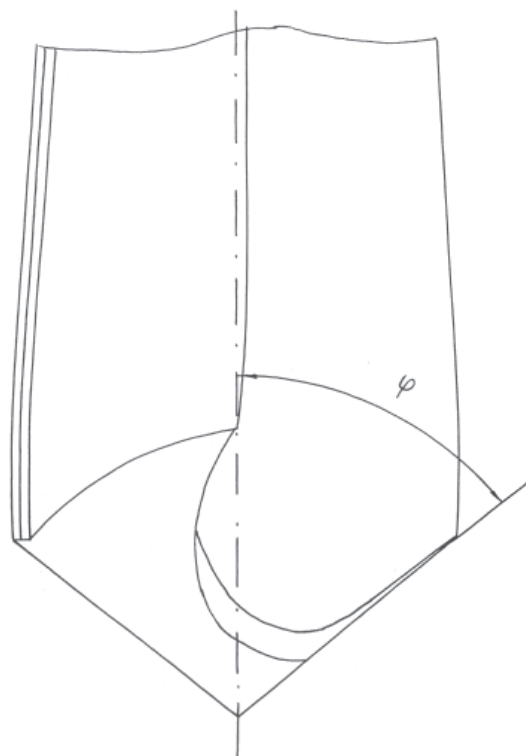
Цилиндрическое сверло с конической заточкой режущей части
